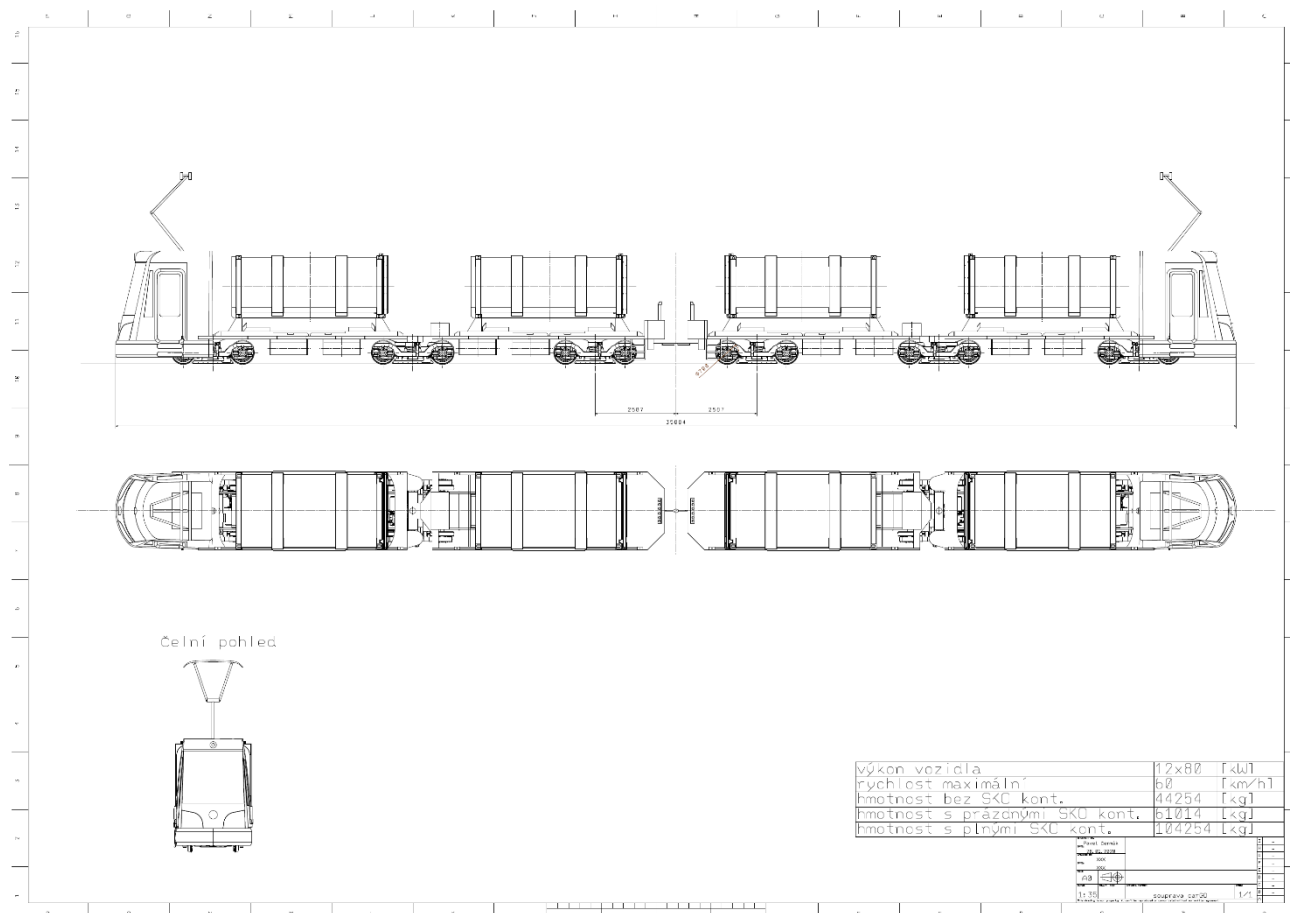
Zmenšený typový výkres Cargo tramvaje.
